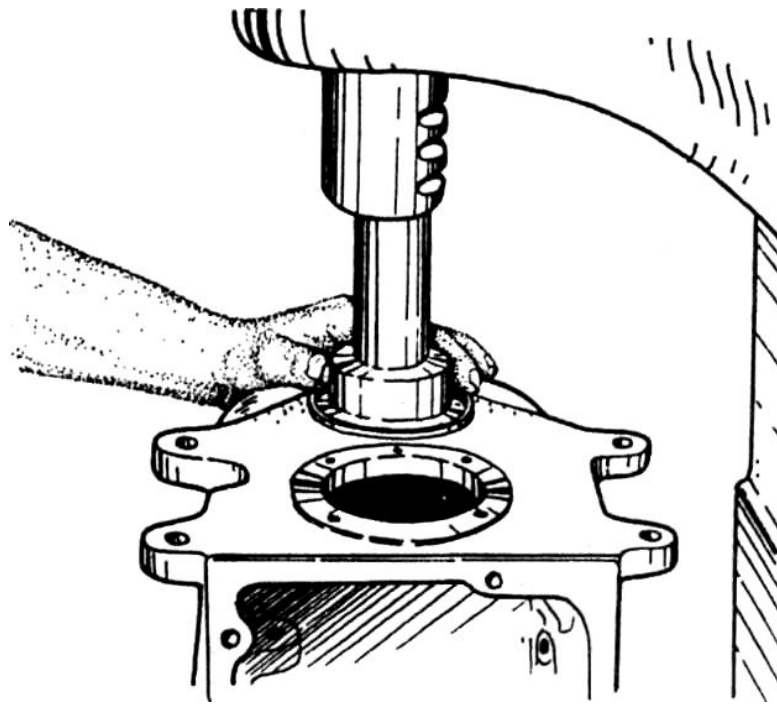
Запресування заглушки переднього підшипника проміжного валу.
